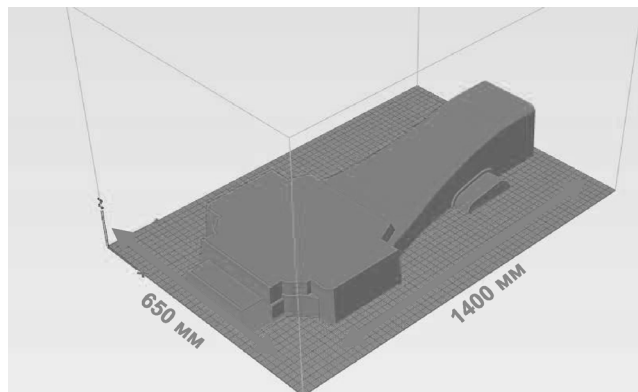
Макет модели корпуса редуктора изготовленный BigRep (ФРГ) [2]
